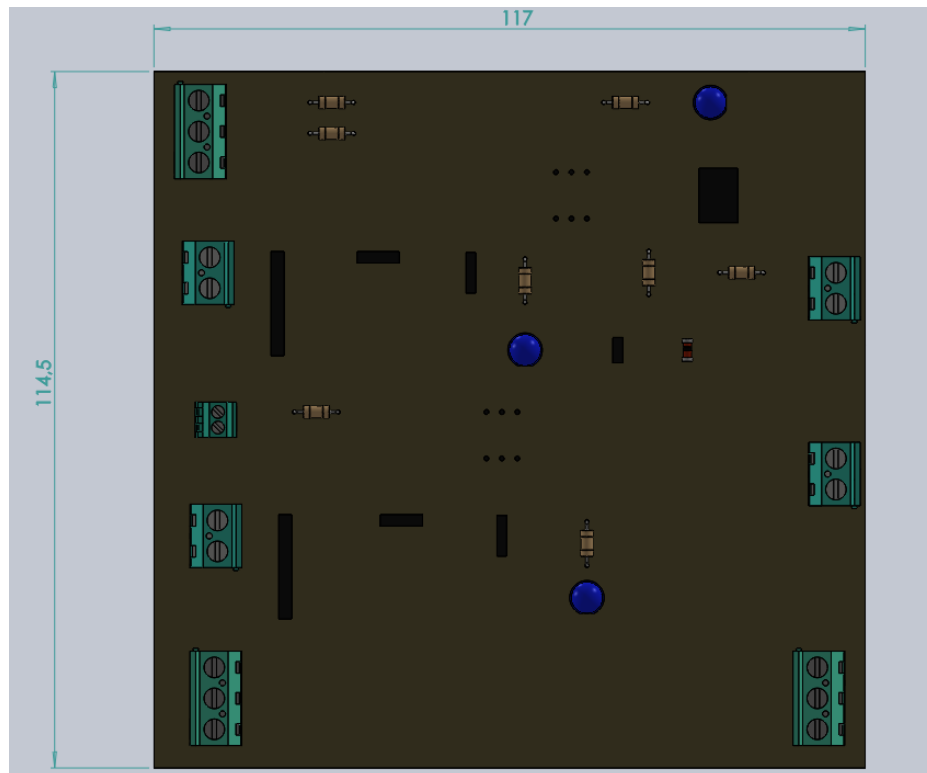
18. Dimensiones de la placa de circuito de control. Fuente: Elaboración propia.
